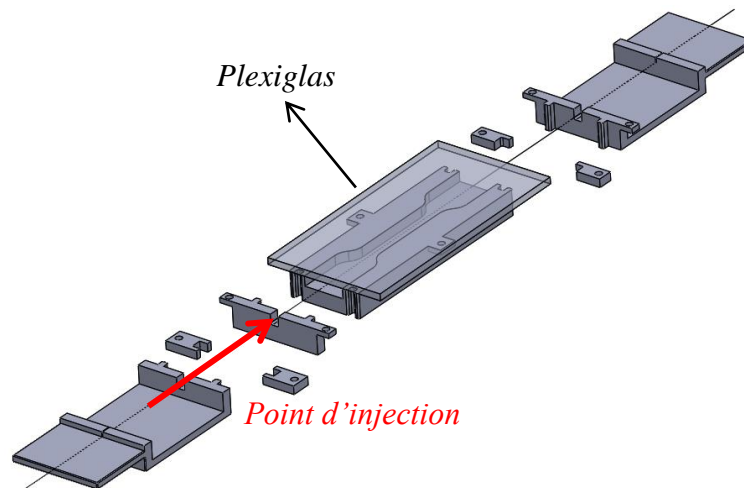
Moule en impression 3D pour insérer un capteur à réseau de Bragg au sein d'une éprouvette type "haltère" par injection
